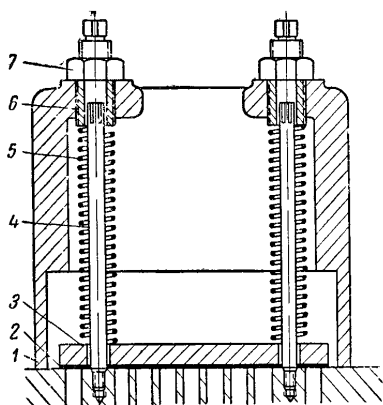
Пластинчатый выхлопной клапан насоса ВН-1.
